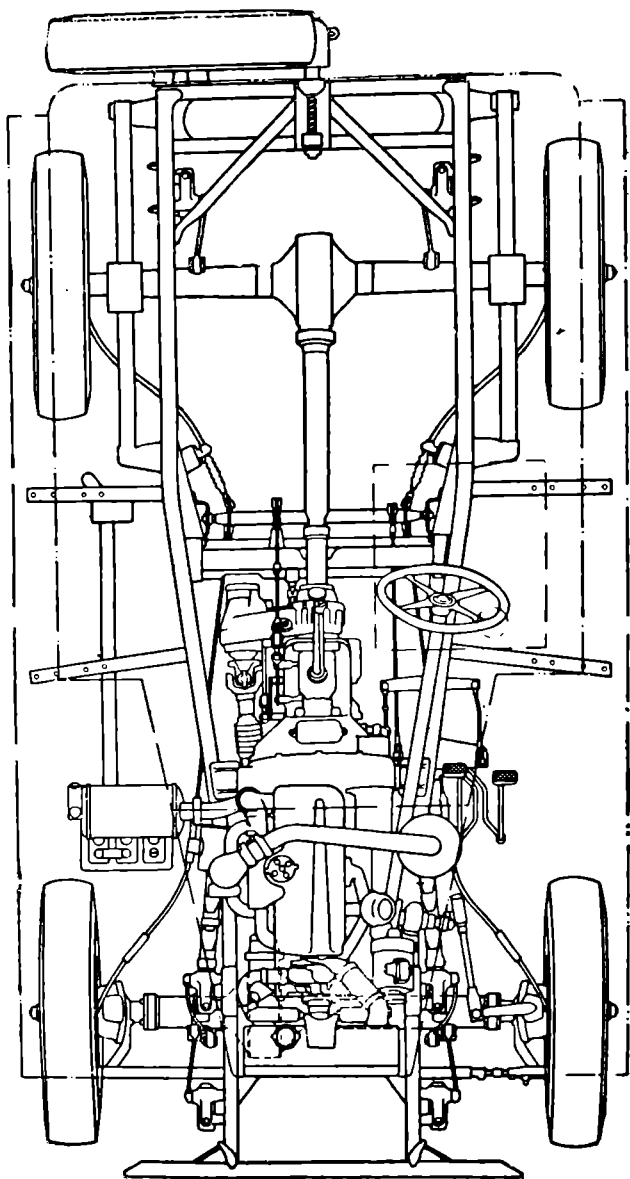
Автомобиль ГАЗ-67Б (чертеж общего вида сверху).
